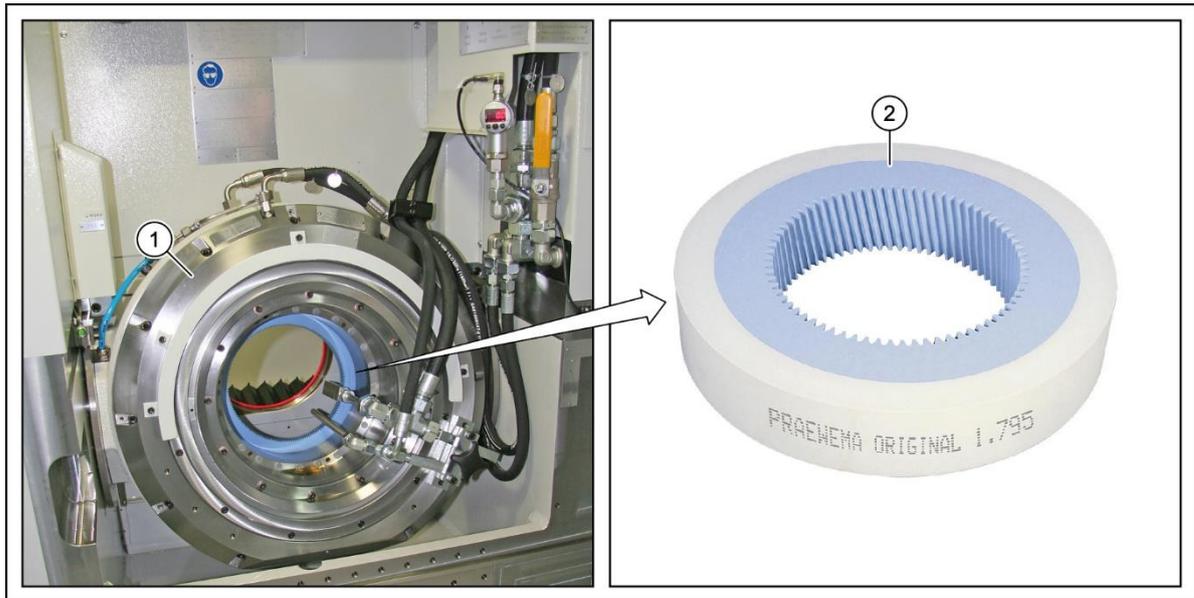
Honkopf mit Honwerkzeug - SynchroFine
